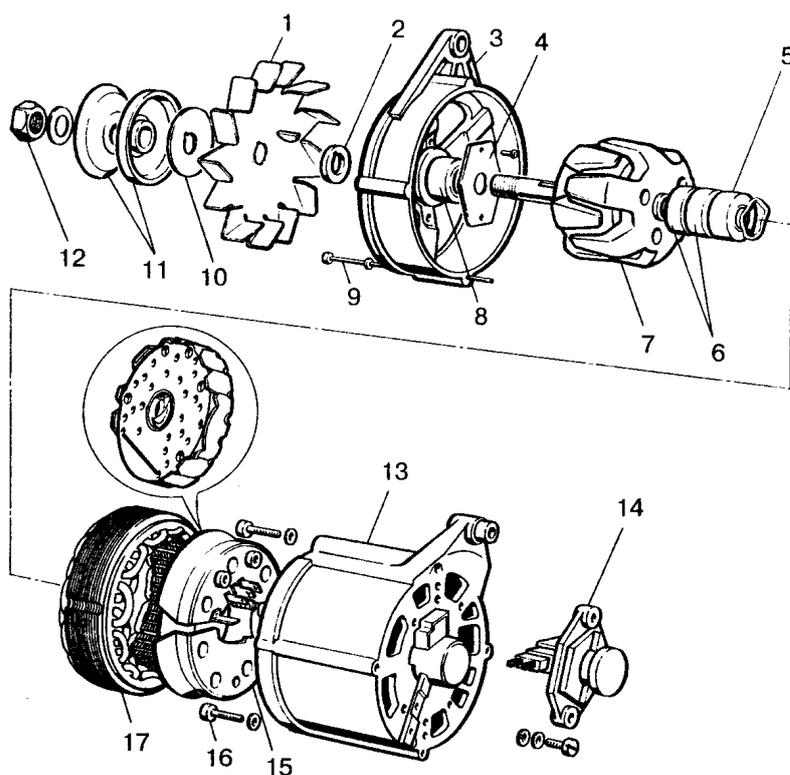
Разборка генератора Bosch: 1 - крыльчатка вентилятора, 2 - шайба, 3 - передняя крышка. 4 - удерживающая пластина, 5 - задний подшипник. 6 - контактные кольца, 7 - ротор, 8 - передний подшипник, 9 - стяжной болт, 10 - промежуточная шайба.
